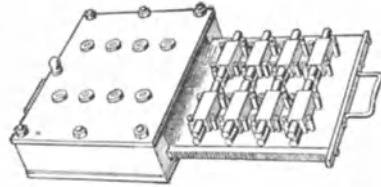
Schubkastenartige Bohrvorrichtung für Mehrspindelbohrmaschinen.
